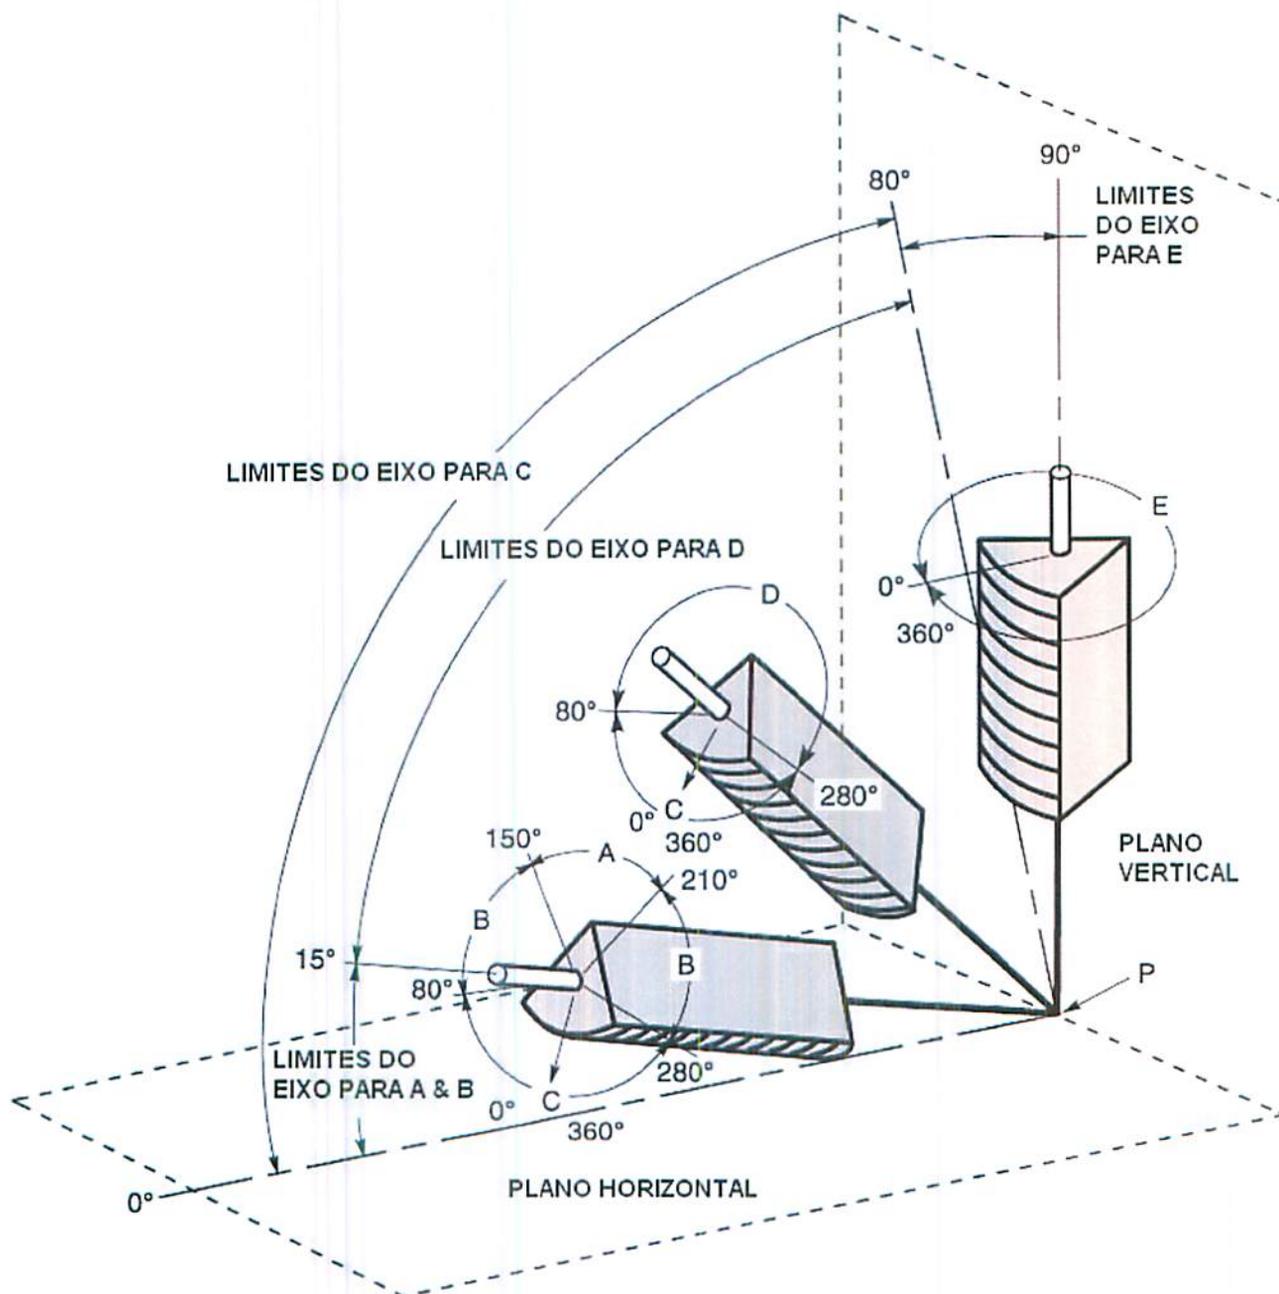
Diagrama para as posições de soldagem de solda em chanfro em chapas
